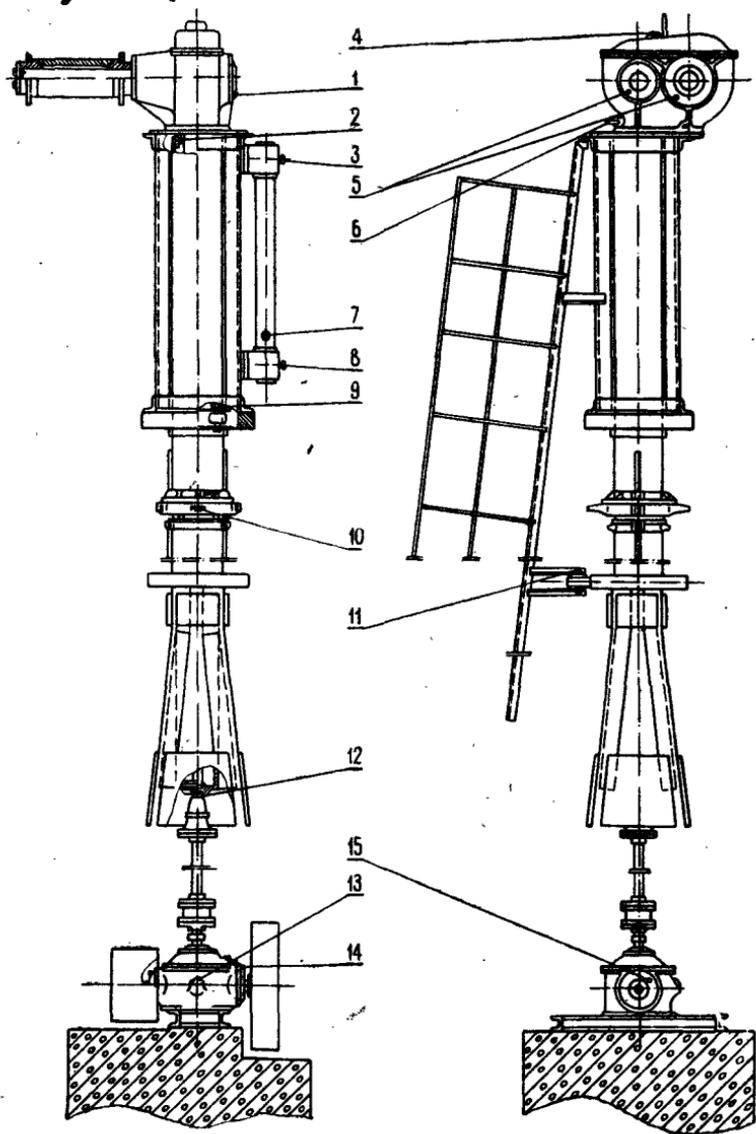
Схема смазки ветродвигателя УВД-8 (см. табл. 22).
